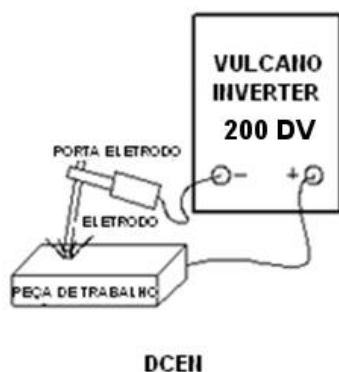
Conexão negativa para soldagem com eletrodo revestido
